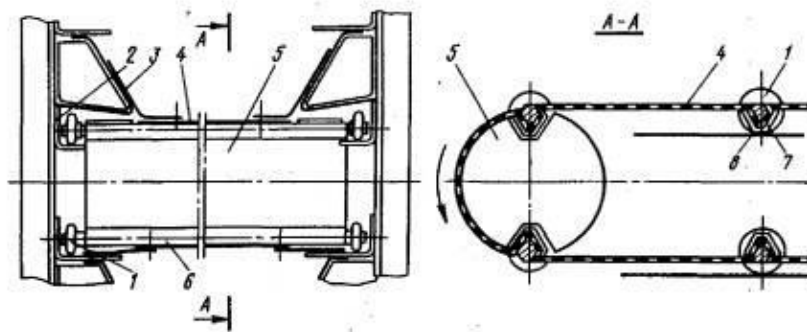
Елементи стрічкового конвеєра попередньої сушарки "Брайбанті": 1 – ролик; 2 – куточок; 3 – щиток; 4 – стрічка; 5 – барабан; 6 - неодружена гілка; 7 – стрижень; 8 – профіль
